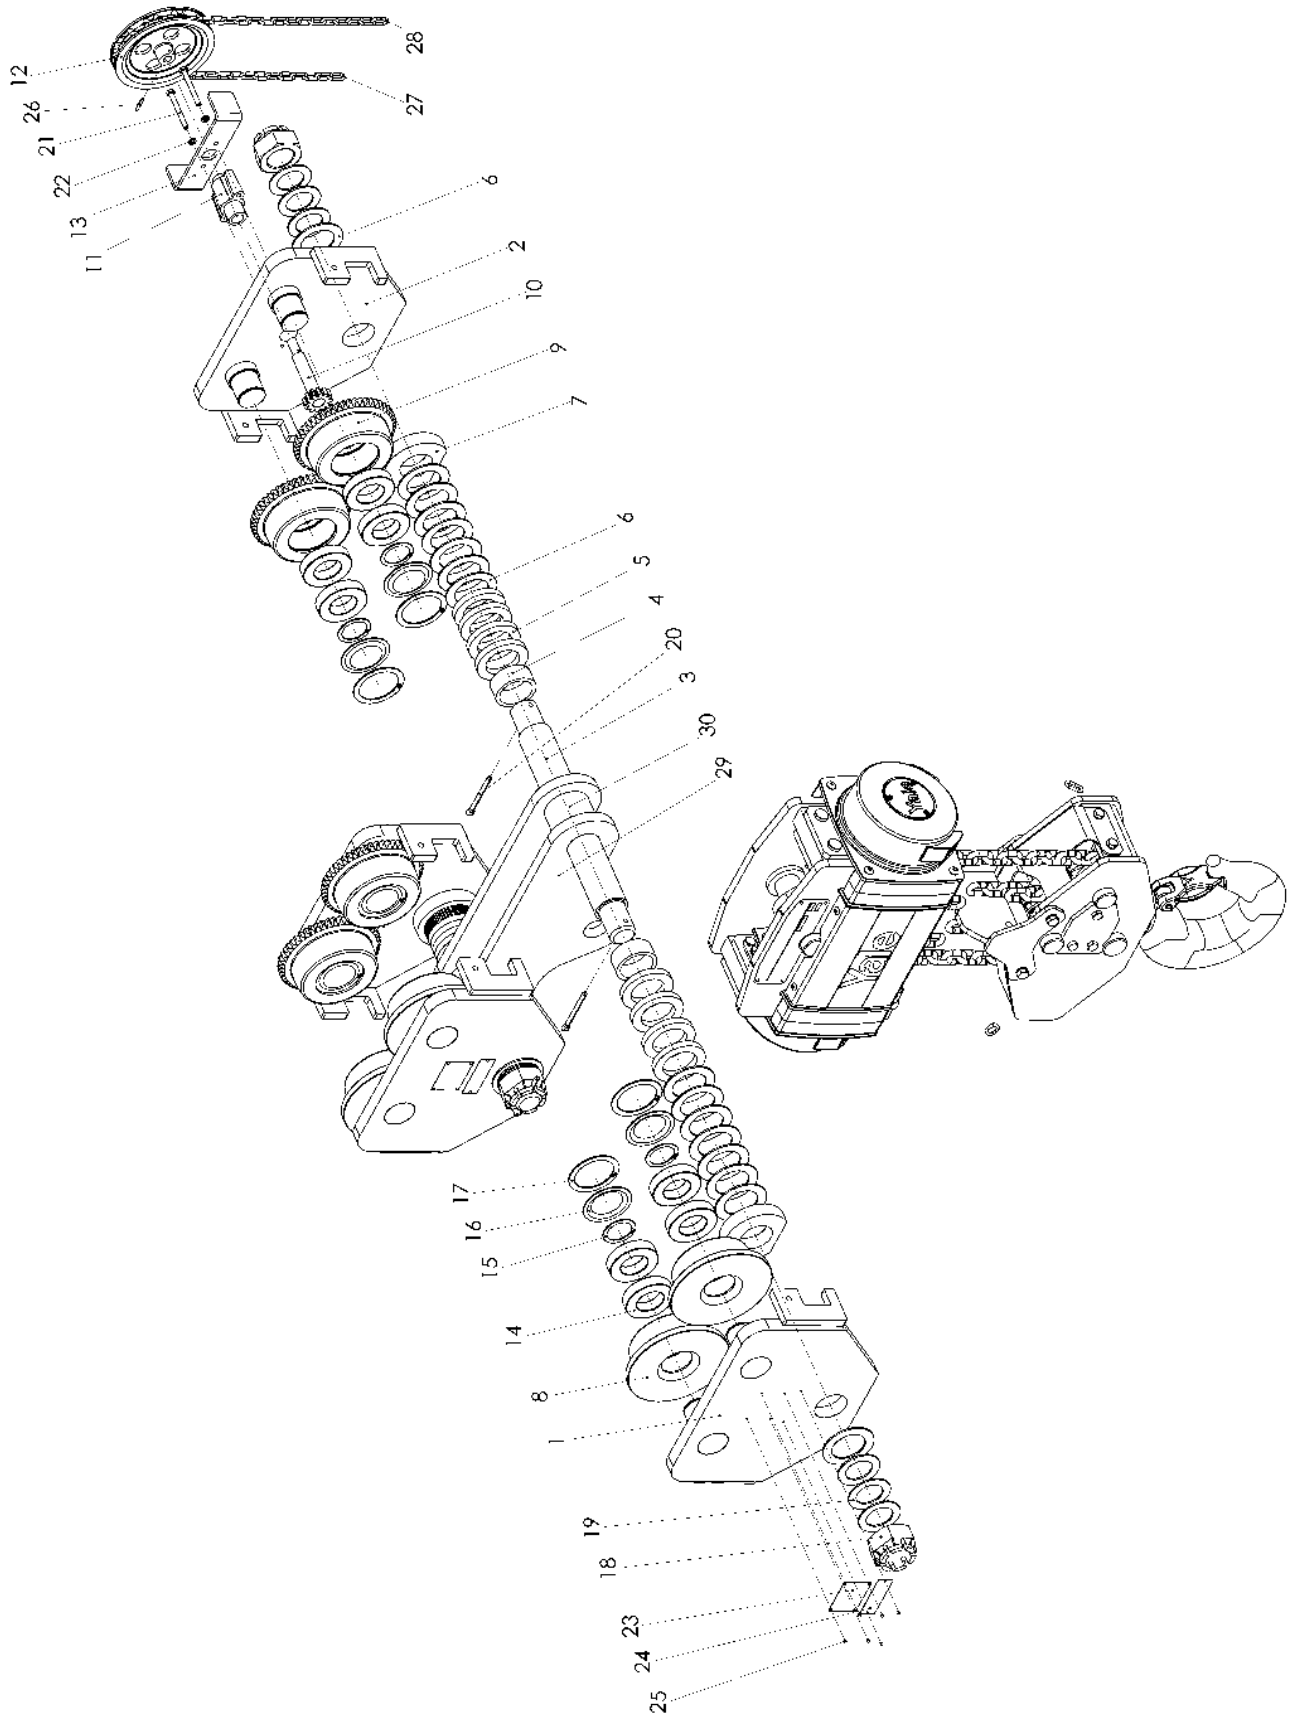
CARRO DE ENGRANAJES DE 15 - 20 TONELADAS
